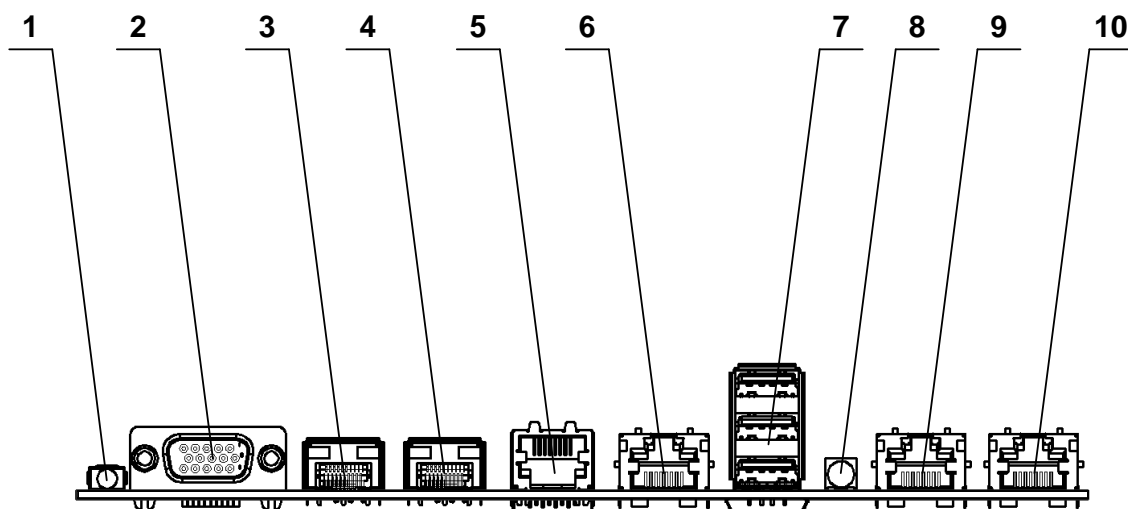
Внешний вид соединителей панели 2Э16С-SPRC
